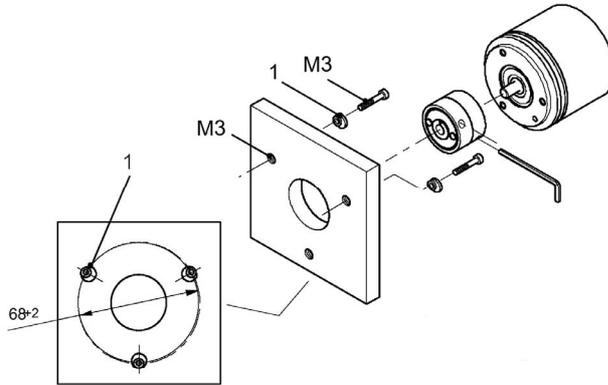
Montaggio: Flangia sincro, 1: Staffa di serraggio
